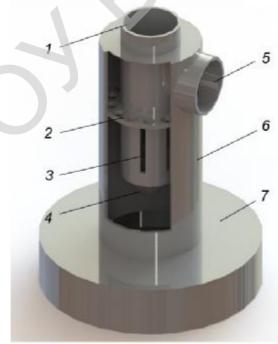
Трехмерная модель классификатора с соосно расположенными трубами: 1 – входной патрубок, 2 – решетка с соосно расположенными трубами, 3 – прямоугольные отверстия, 4 – отверстие, 5 – выходной патрубок, 6 – корпус устройства, 7 – бункер
